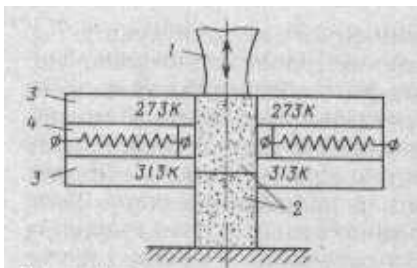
Схема сварки с нагревом зоны сварки и охлаждением зоны детали, контактирующей с волноводом: 1 - волновод, 2 - свариваемые детали; 3 - медные радиаторы; 4 - термобатарея
